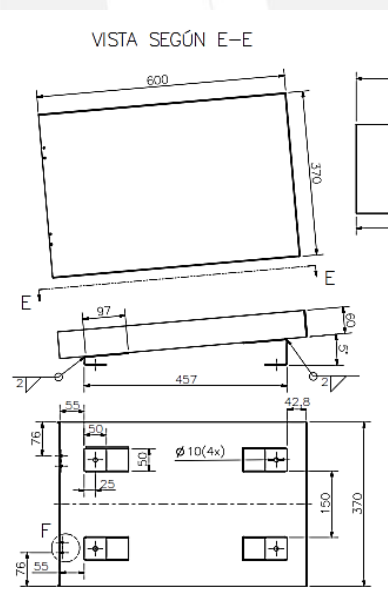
Plano de bandeja huevos rechazados – Plano PD1.1.3-A2
